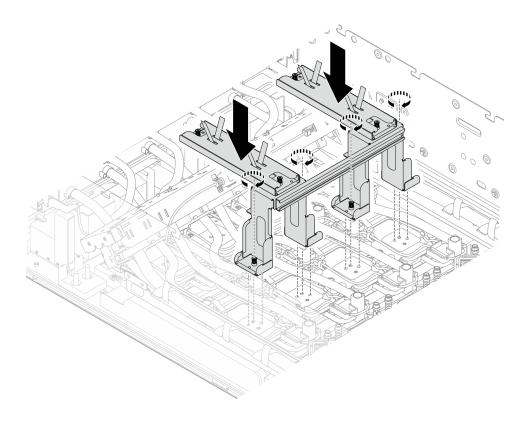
Installazione delle staffe di spedizione sulle piastre a freddo della GPU posteriore
